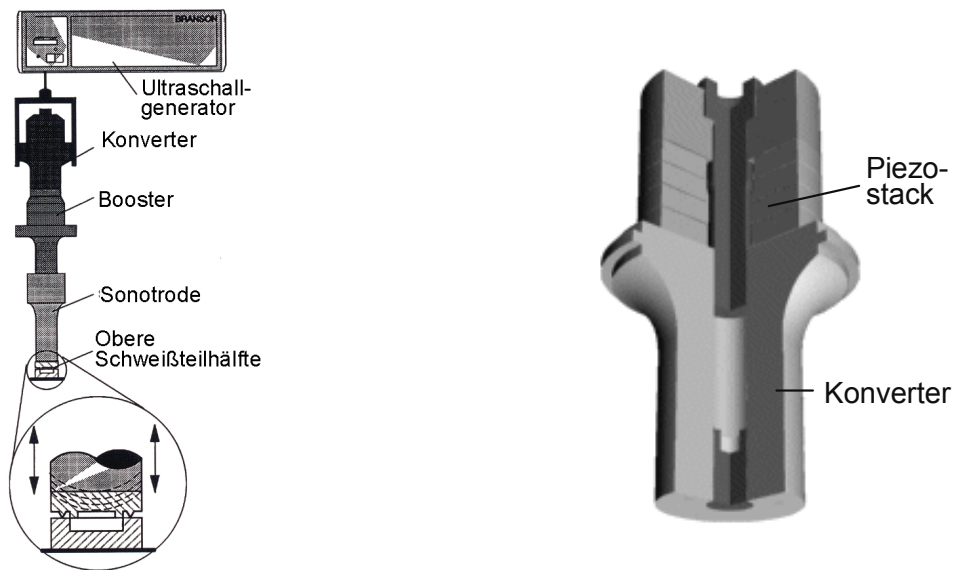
Funktionsprinzip Ultraschallschweißen (links) mit Konverterinnenansicht (rechts) [64].
